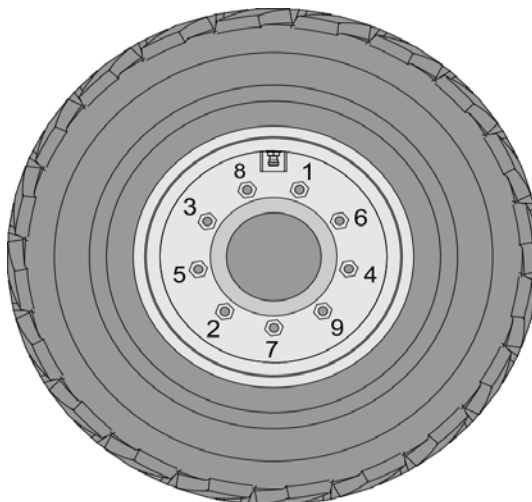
Порядок затяжки крепежной гайки колеса
